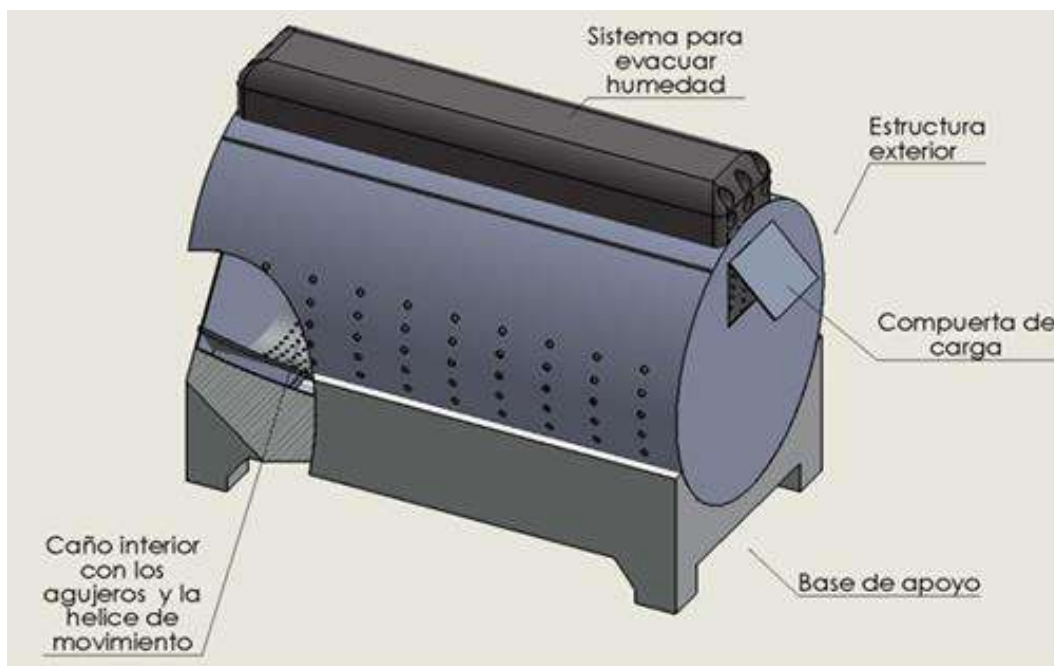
“Propuesta de cilindros horizontales con detalle de elementos”
